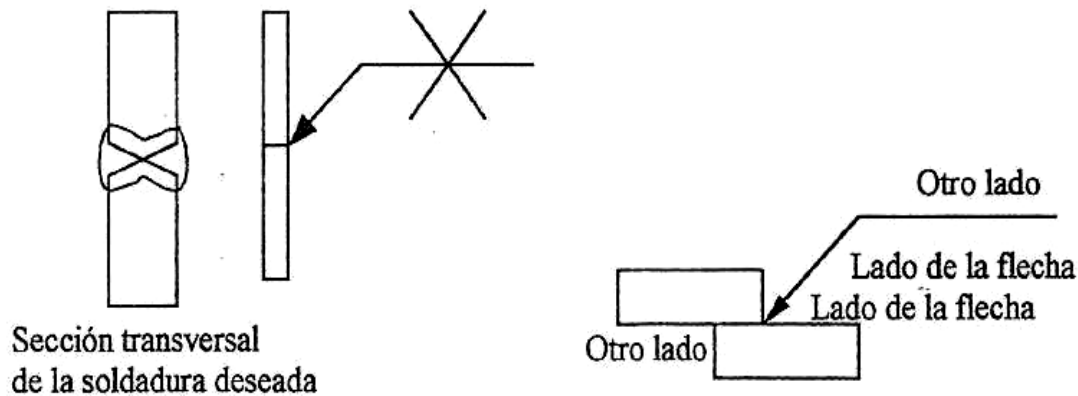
Símbolo para una soldadura de ranura en "V" por ambos lados de la flecha
